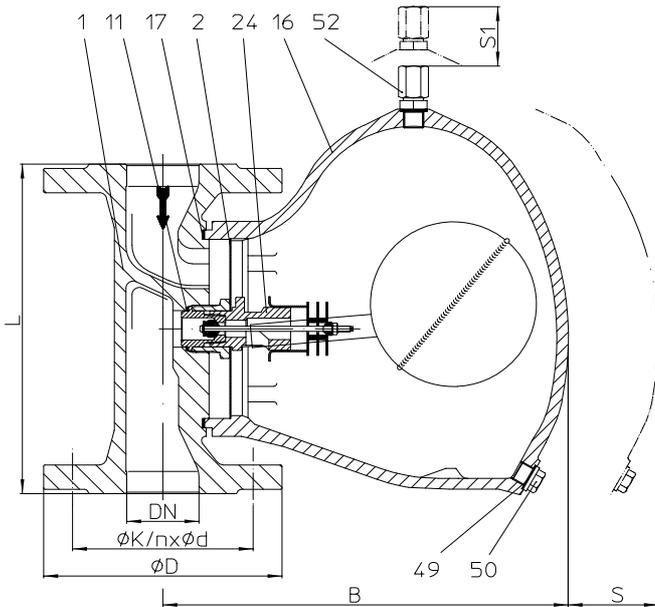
1 mit Flanschen - vertikale Einbaulage
